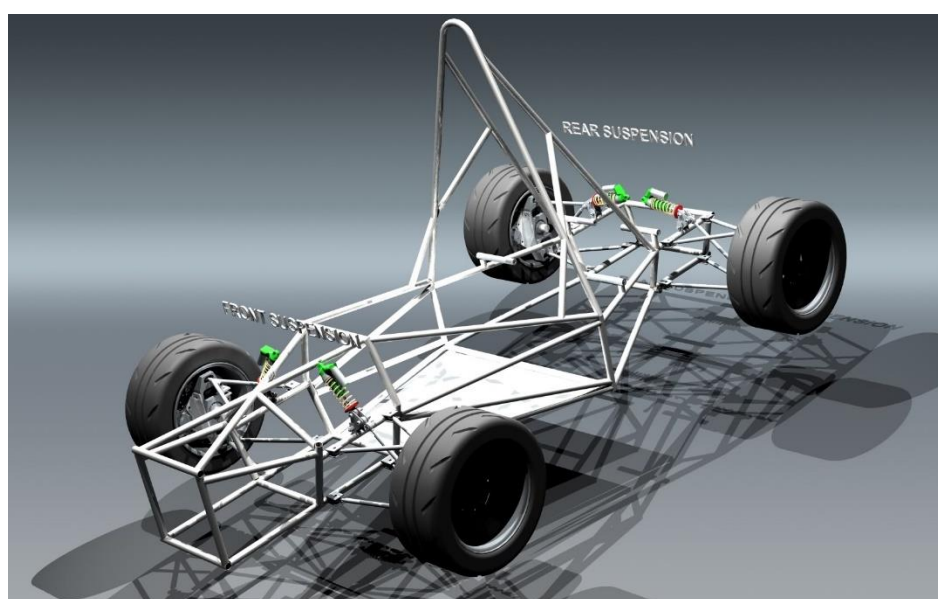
Chassis tubular de um Fórmula SAE. [8]
